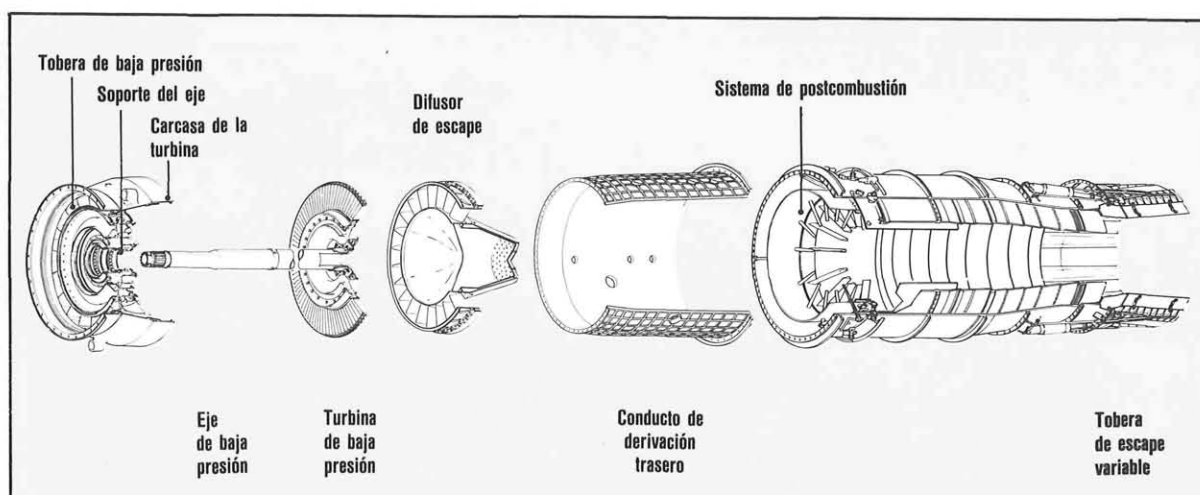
Módulos del motor en los que se incluyen los de SENER.
